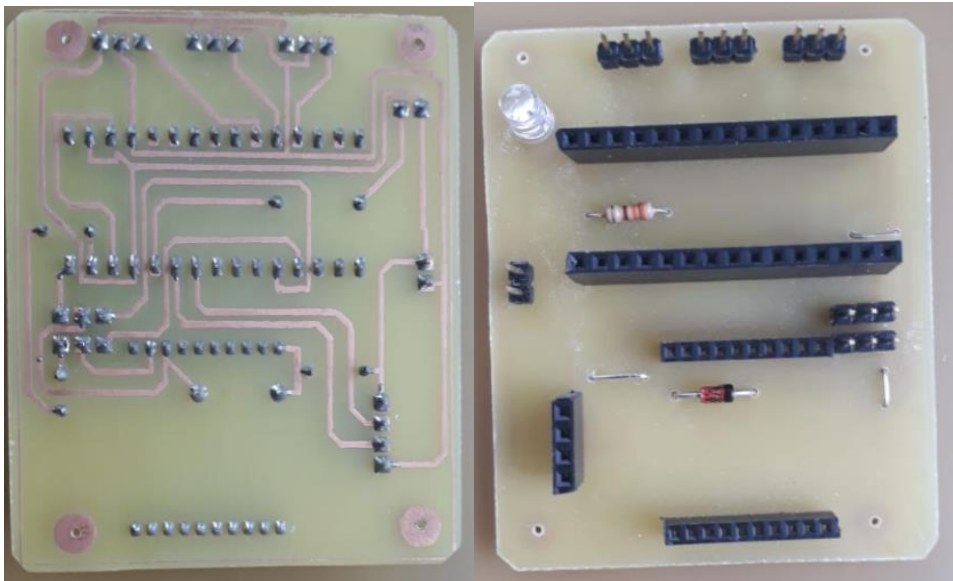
Construcción de la placa electrónica *Printed Circuit Board* (PCB) Para el Nodo 1
